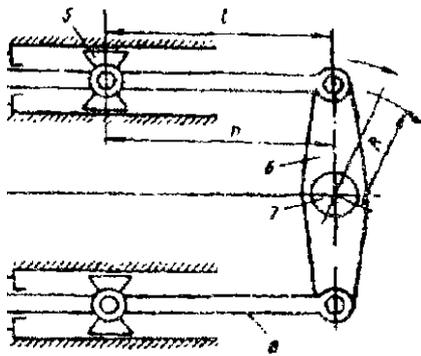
Плунжерный привод с цилиндрами двойного действия:
